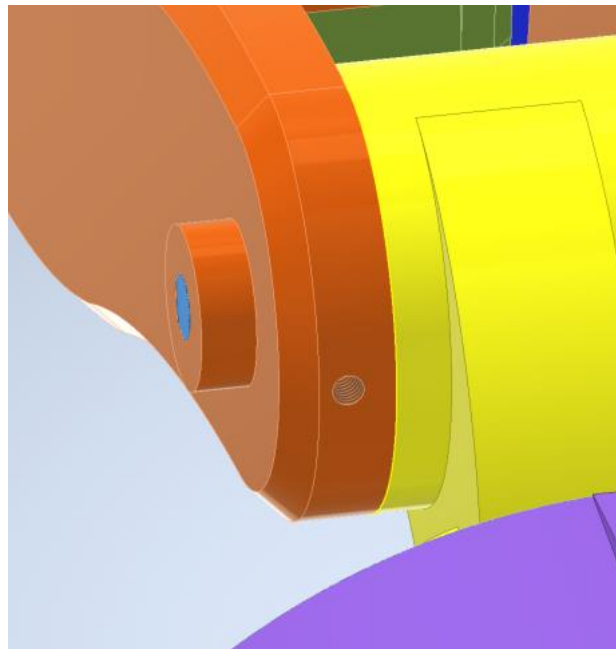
Tornillo prisionero motor hombro segundo diseño
